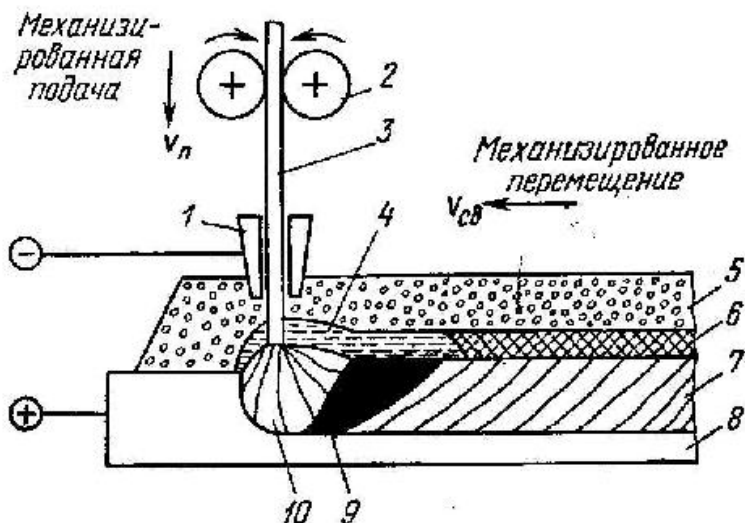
Схема автоматической дуговой сварки
